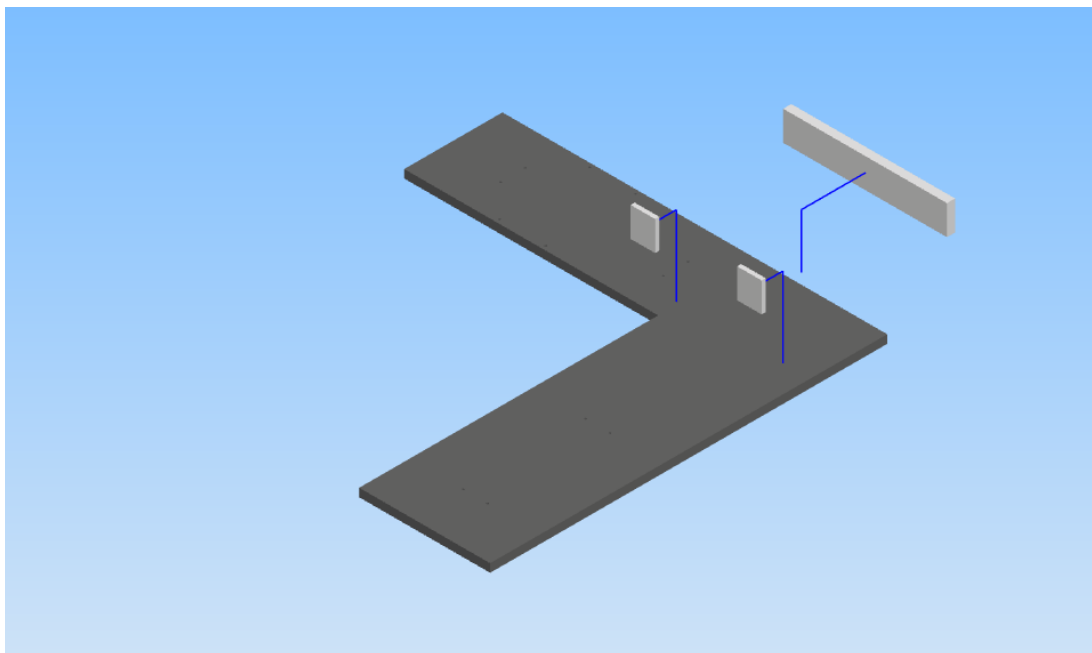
Vista explosionada del ensamble mostrado en la figura 3.52.
